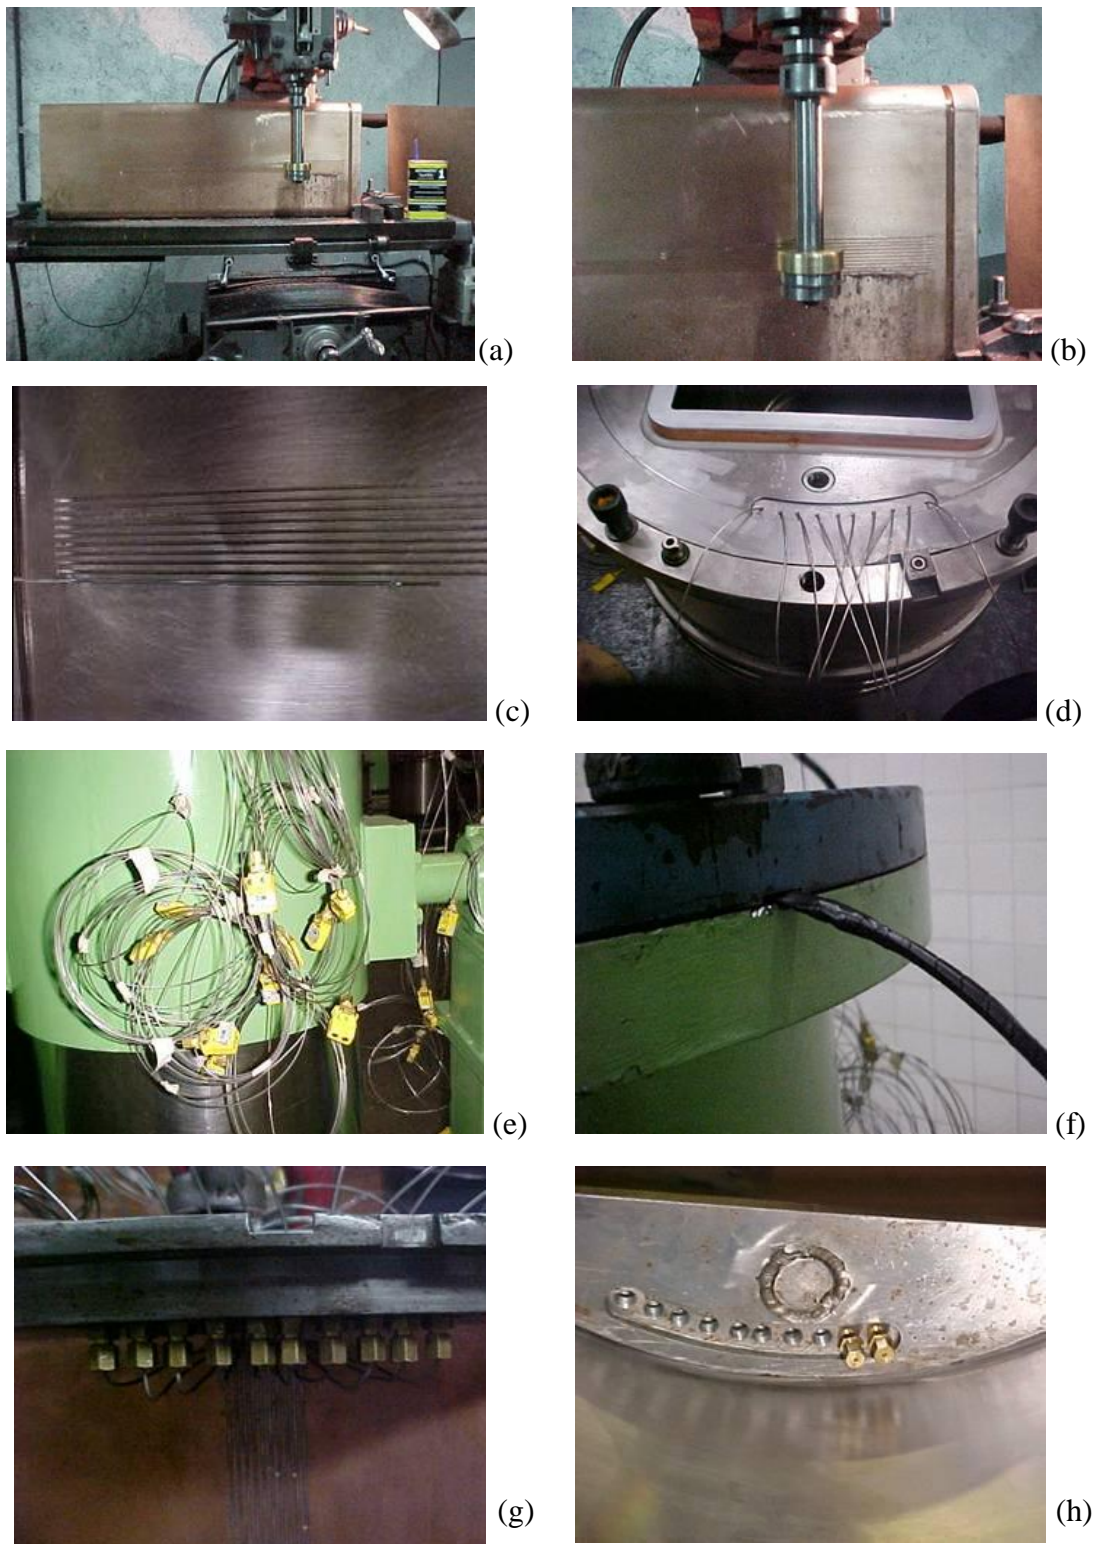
Sequência de usinagem e montagem dos termopares no molde: (a) e (b) usinagem, (c) detalhe dos sulcos para passagem dos termopares, (d) termopares inseridos no molde, (e) e (f) sistema de conectores e cabos de compensação, (g) e (h) terminais para acoplamento entre os termopares e os cabos de compensação.
